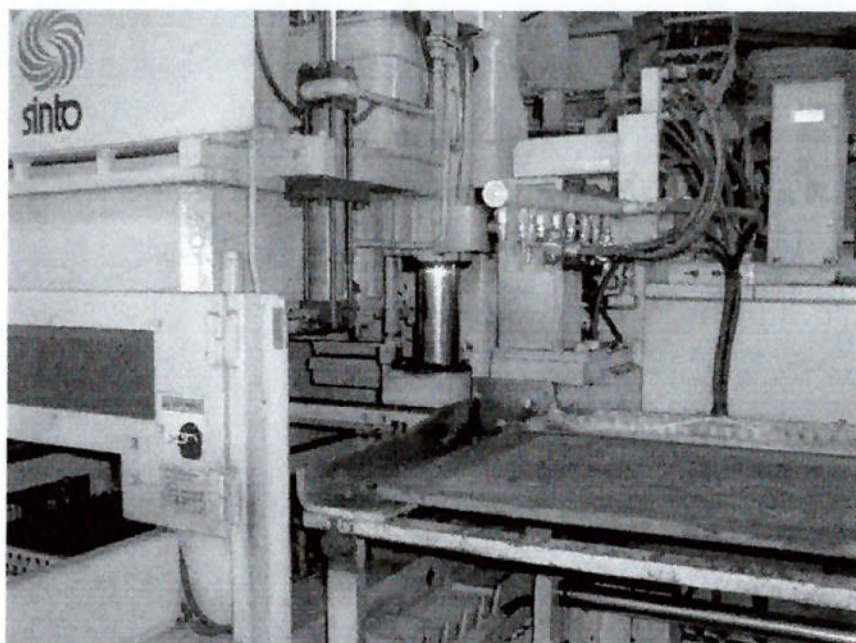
Equipamento para moldagem automática fabricado pela empresa Sinto, modelo FBO II.
